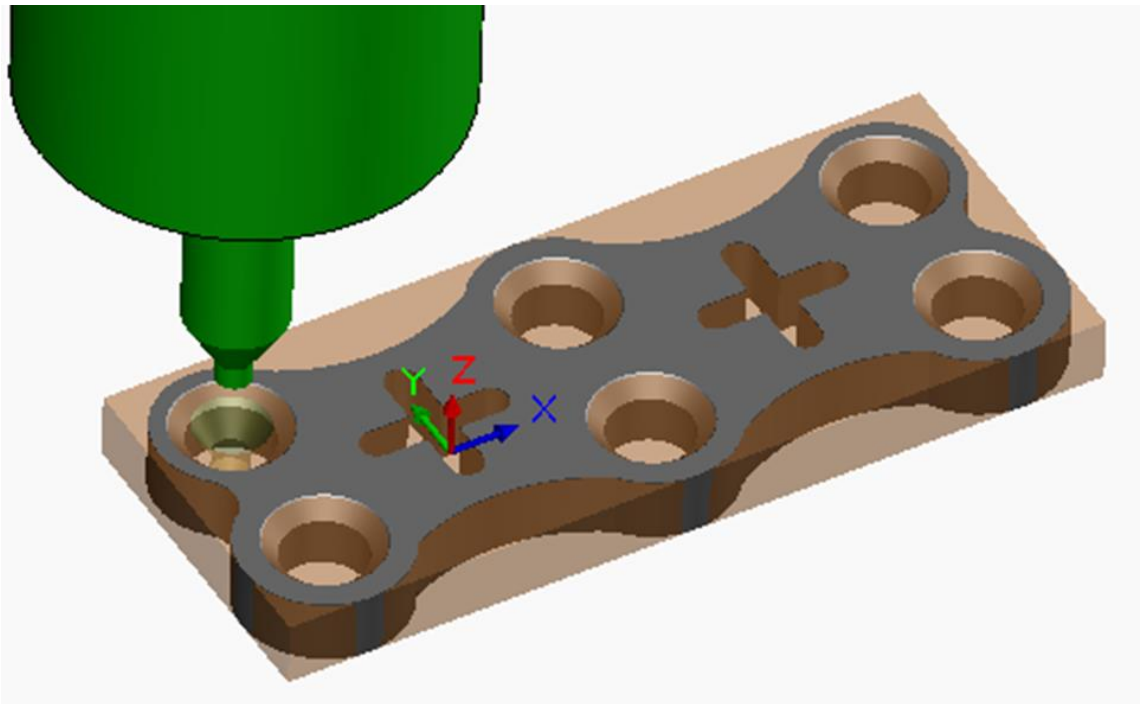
Моделювання фрезерної обробки пластини-імпланту у САМ-системі
